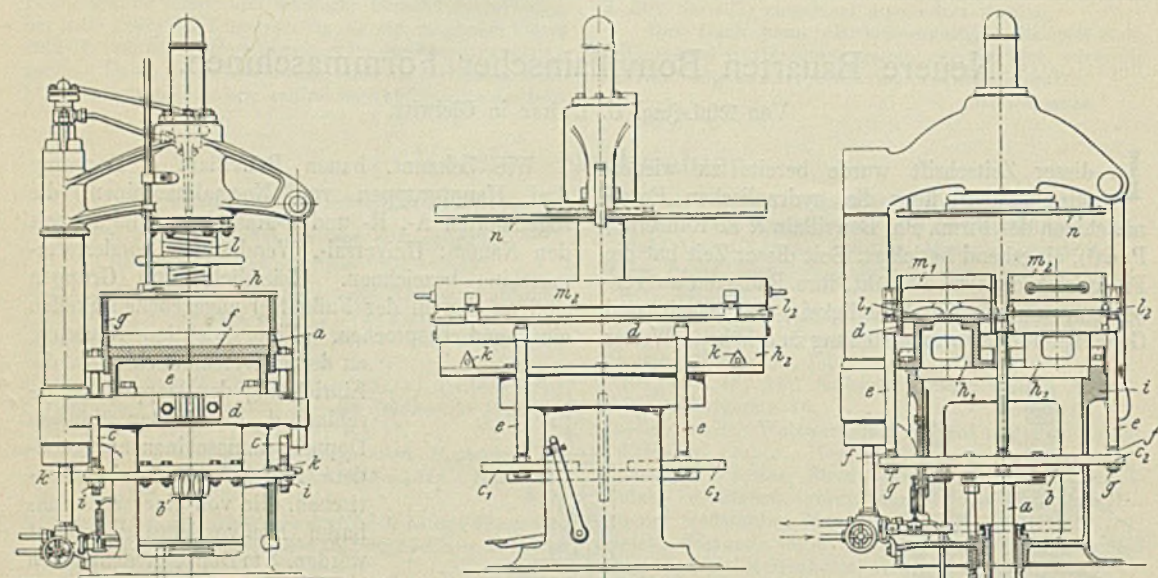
Universalformmaschine A, für Radiatorenformen eingerichtet.
